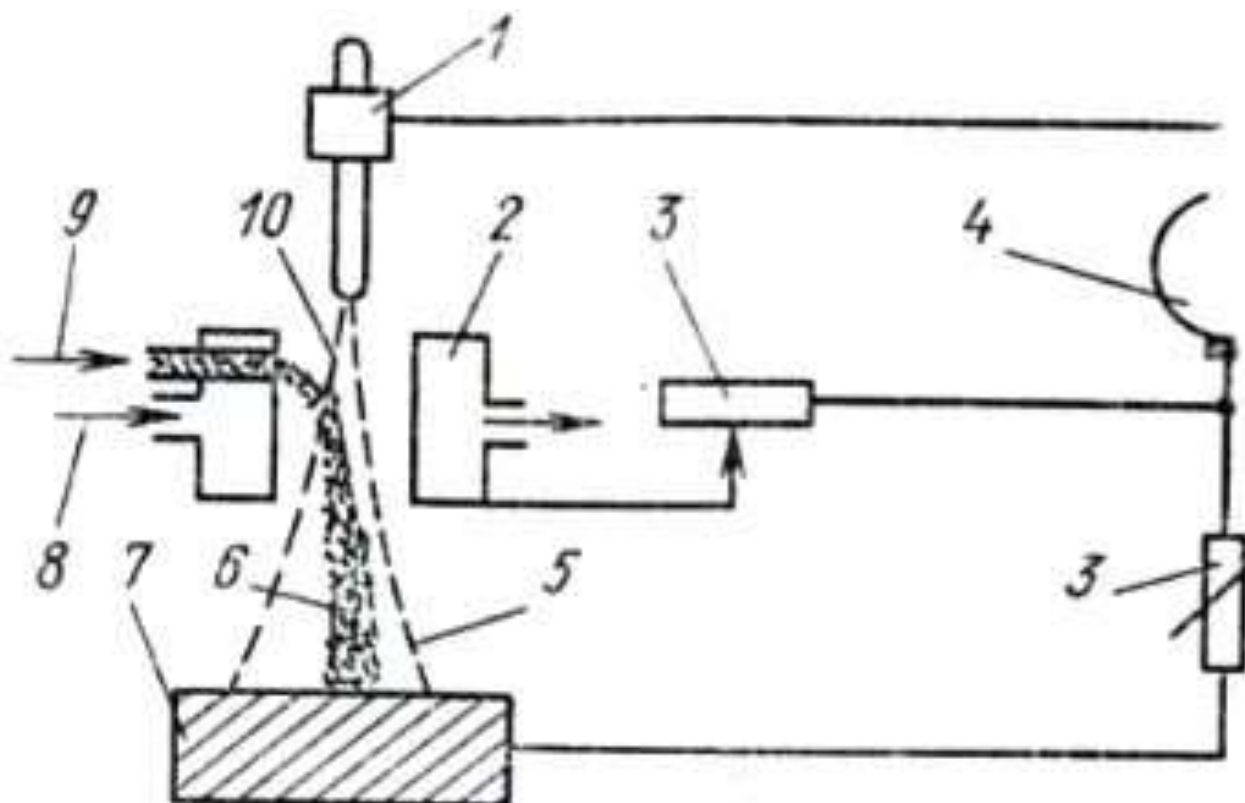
Схема установки для плазменной наплавки порошковым материалом: 1 — вольфрамовый электрод; 2 — сопло плазматрона; 3 — электросопротивление; 4 — источник электропитания; 5 — плазменная струя; 6 — плазменный факел; газ и частицы присадочного материала; 7 — восстанавливаемая деталь; 8 — система подачи воды для охлаждения электродов; 9 — газ, транспортирующий порошок; 10 — плазмообразующий газ.
